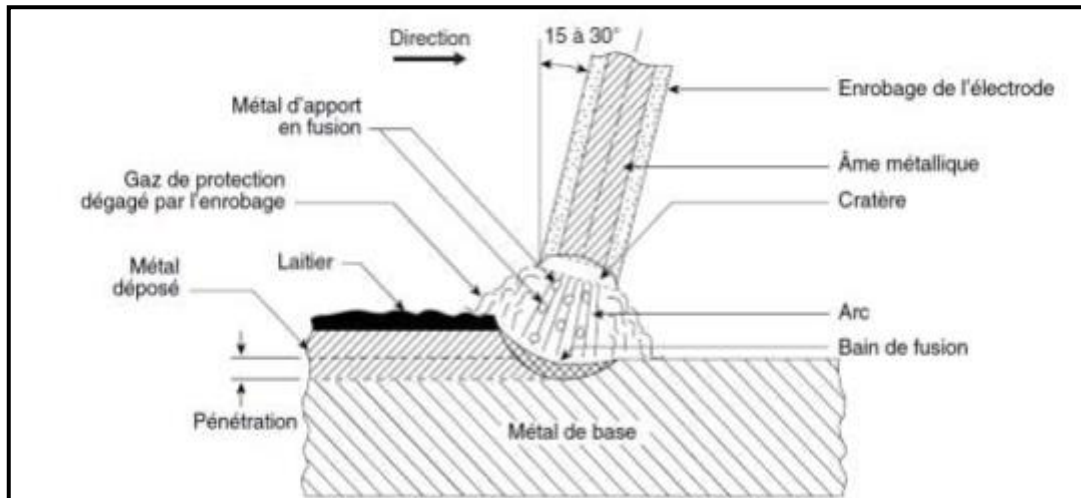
Principe de la procédé du soudage SMAW [29]
